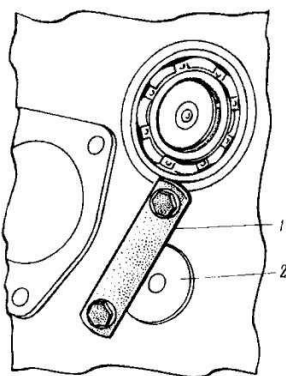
Снятие стопорной планки оси промежуточной шестерни: 1 — стопорная планка; 2 — ось промежуточной шестерни
